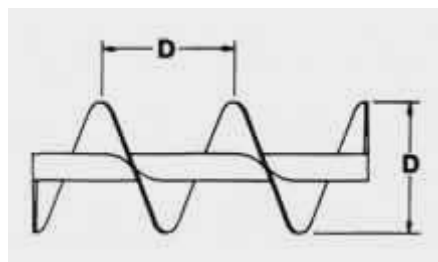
Tornillo estándar. Fuente: <http://www.kwsmfg.com/services/screw-conveyor-engineering-guide/conveyor-flight-pitch-types.htm>
